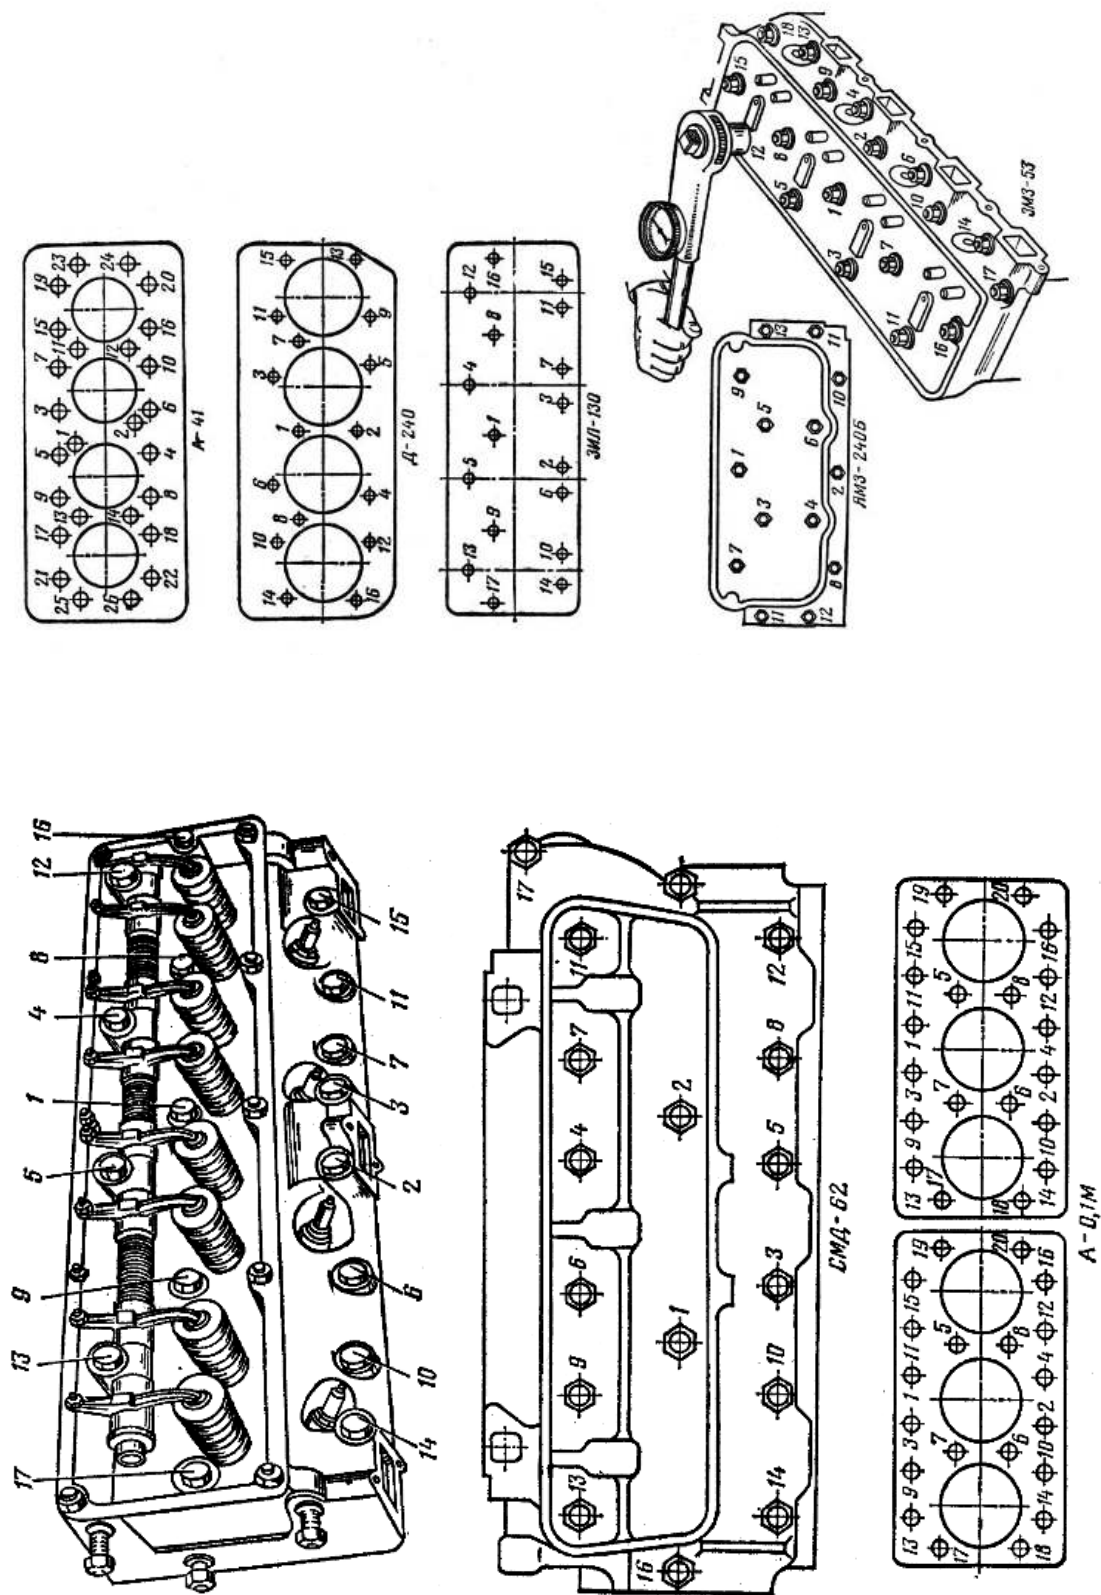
Последовательность затяжки гаек крепления головок цилиндров двигателей
